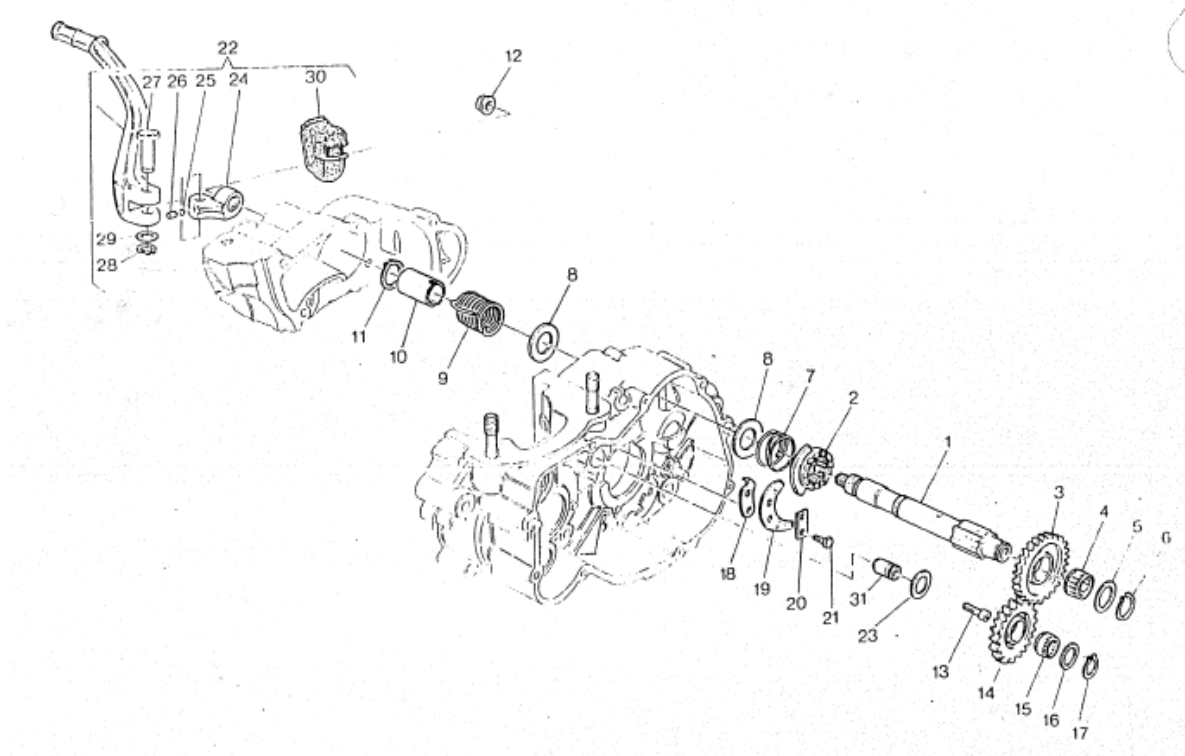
Despiece de los engranajes del pedal de arranque.
